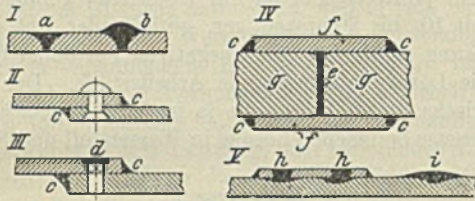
Beispiele elektrischer Reparaturschweißungen.
